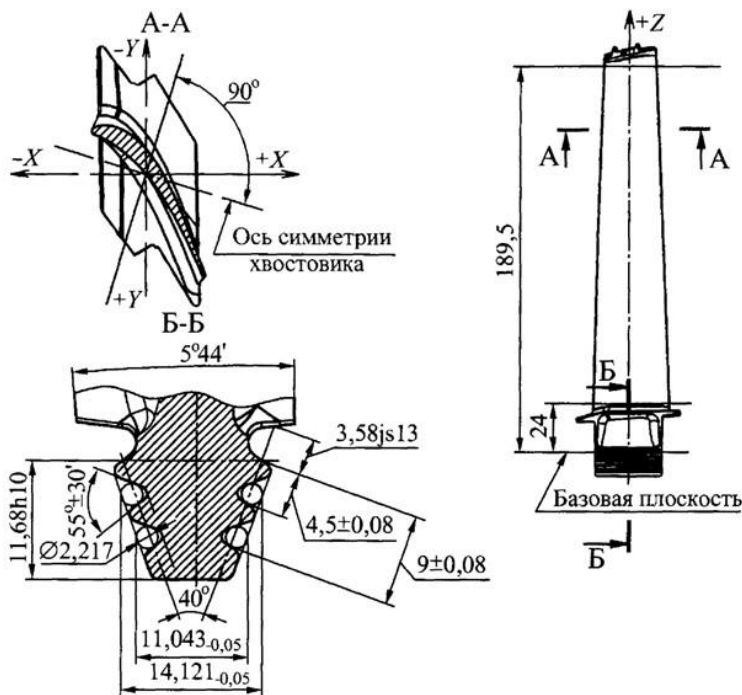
основні конструктивні елементи робочої лопатки турбіни, що формуються механічною обробкою.
